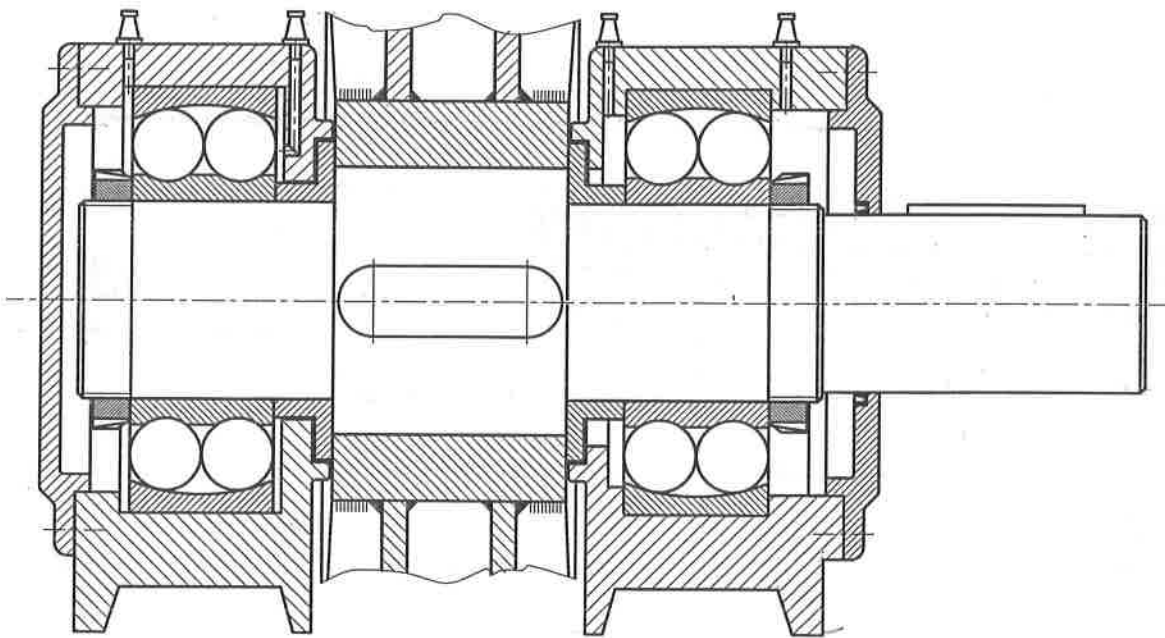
Disposición de rodamientos. Rodamientos de bolas a rótula. Rodamiento libre a la izquierda y rodamiento fijo a la derecha.
